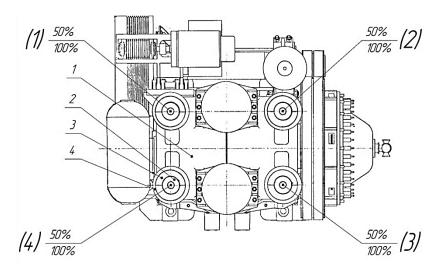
Схема установки и последовательности затяжки гидрогаек: 1 – станина; 2 – стяжная шпилька; 3 – гидрогайка; 4 – проставка
